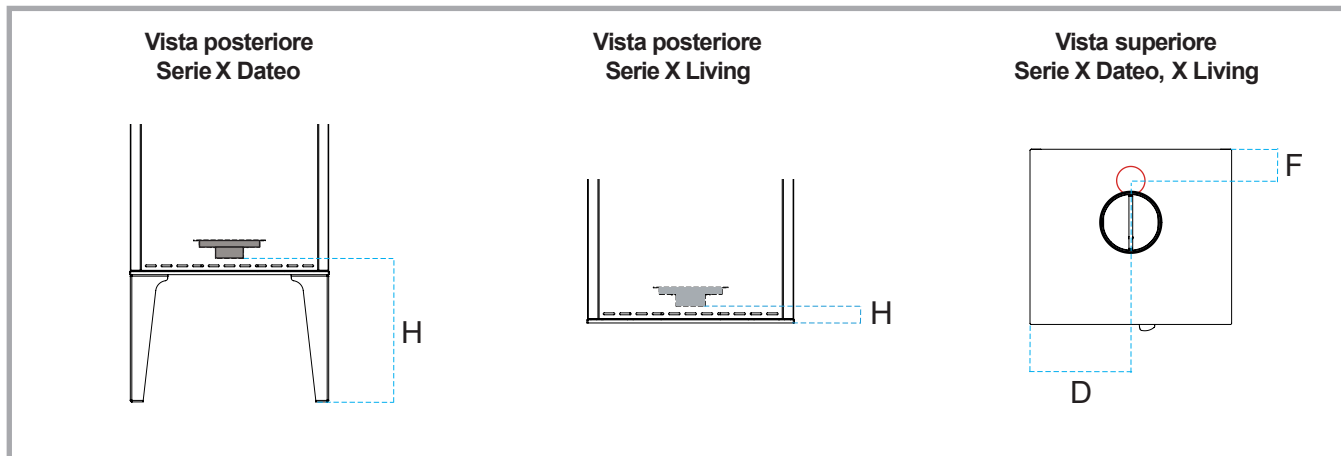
B - Vista superiore e posteriore della stufa a legna e specifiche per il collegamento con la presa d'aria esterna.
